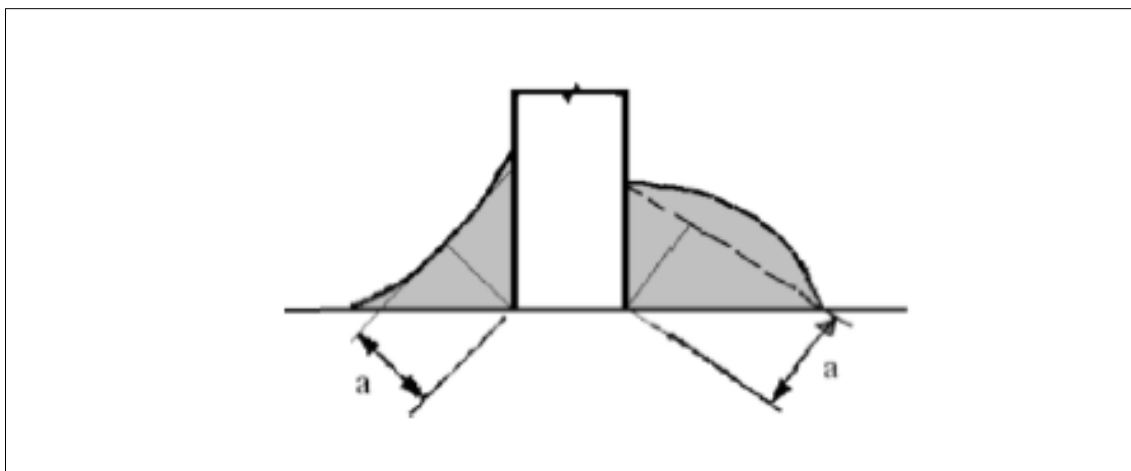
Gorge d'une soudure d'angle.
